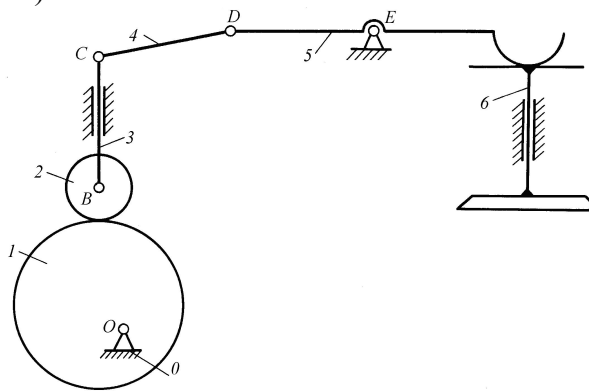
Газорозподільний механізм двигуна вертольота
